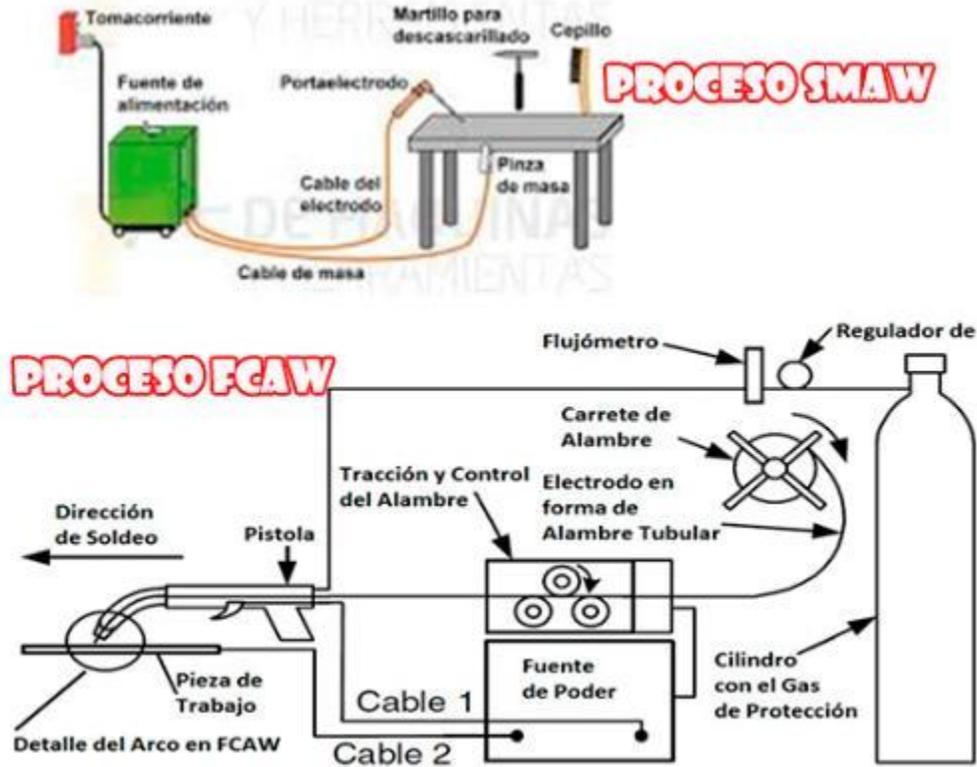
Procesos de Soldadura SMAW y FCAW
